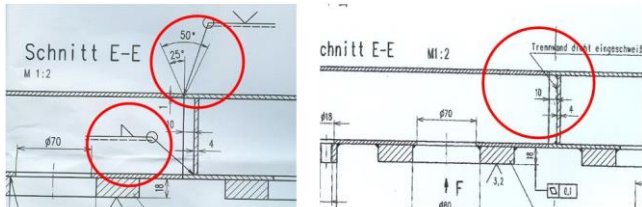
Zeichnung mit exakten Vorgaben - rechte Seite ohne schweißtechnische Angaben
